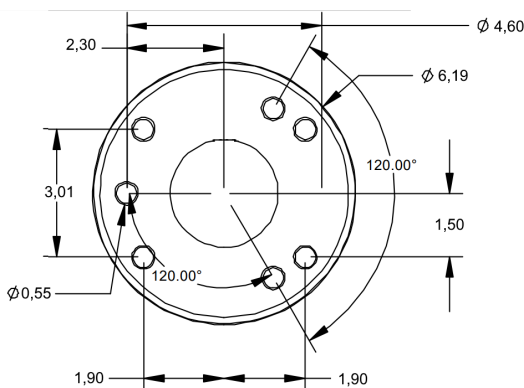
Przygotowanie do montażu na uchwycie RAM
